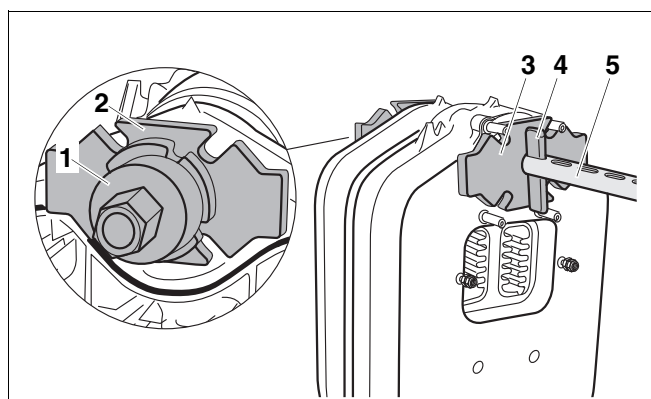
Outil de serrage monté sur le moyeu supérieur
